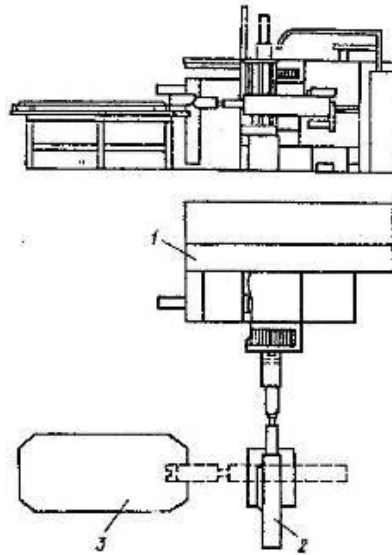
Однопозиционный РТК на базе токарного станка с ЧПУ мод. 16К20Ф3 и промышленного робота М20П40.01: 1 – Токарный станок 16К20Ф3; 2 – Промышленный робот; 3 – Тактовый горизонтальный магазин-накопитель.
